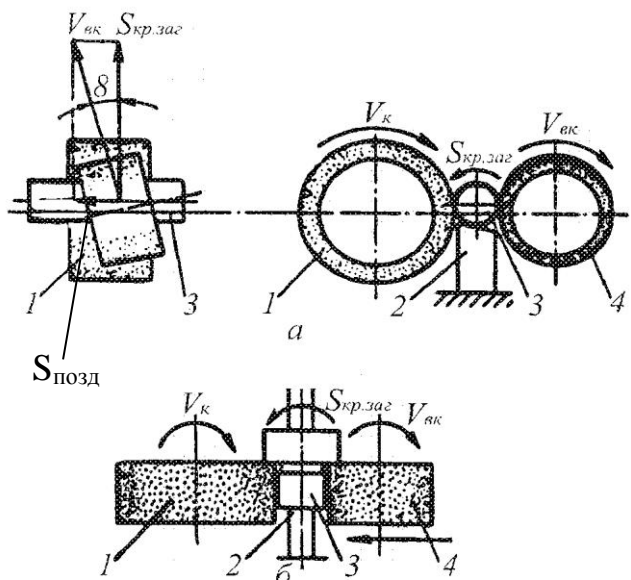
Схеми обробки заготовок на безцентрово-шліфувальних верстатах
